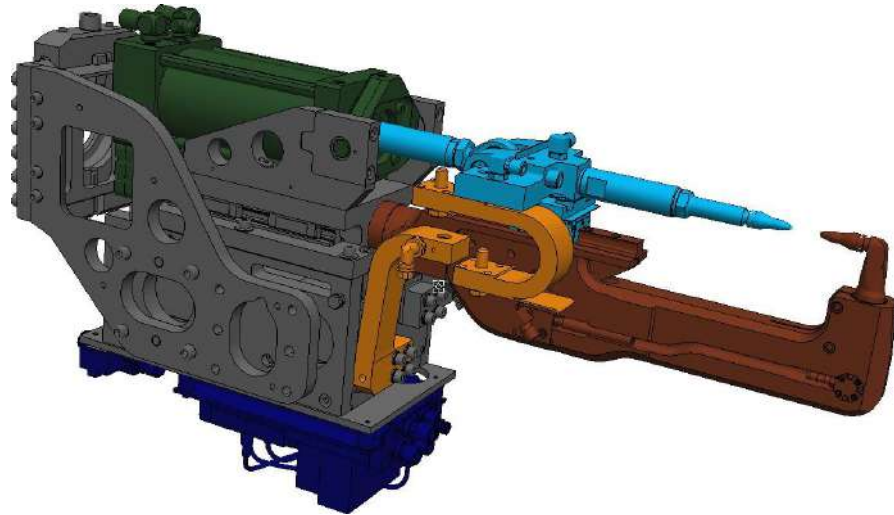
Зварювальний пістолет для стаціонарного зварювання
